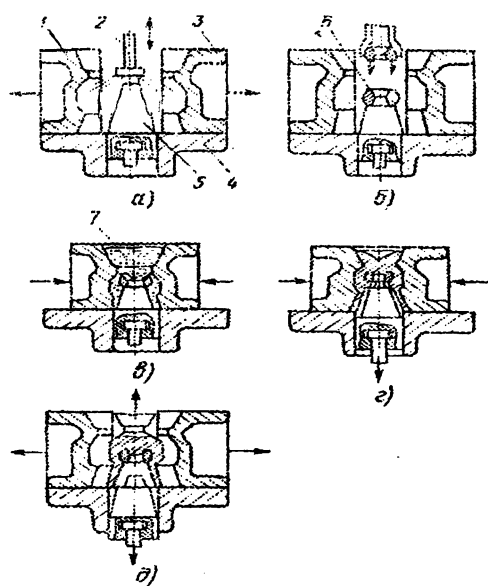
Схема изготовления отливки в металлической форме (кокиле):
